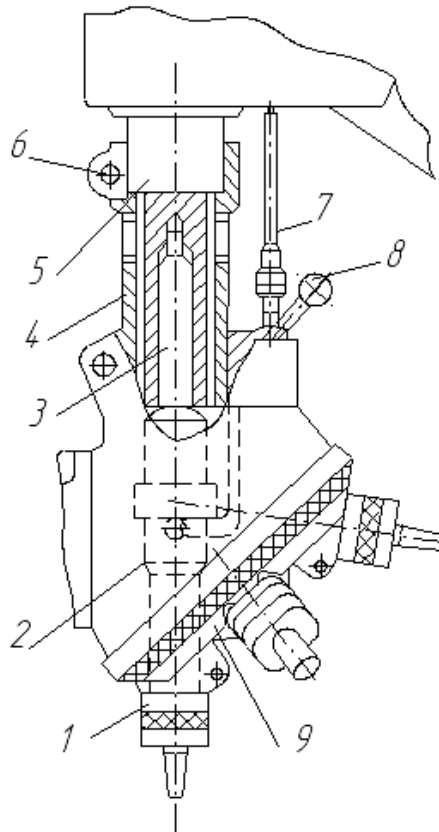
Багатошпindelна револьверна головка для одиночних інструментів
